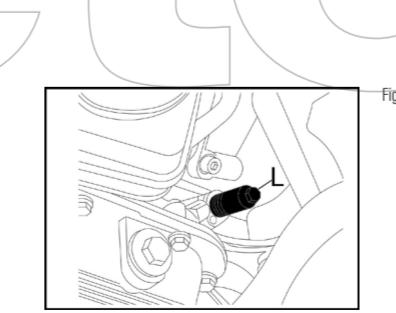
Figura 7: Svitare il tappo sul monoblocco e montare la ditta albero motore.
